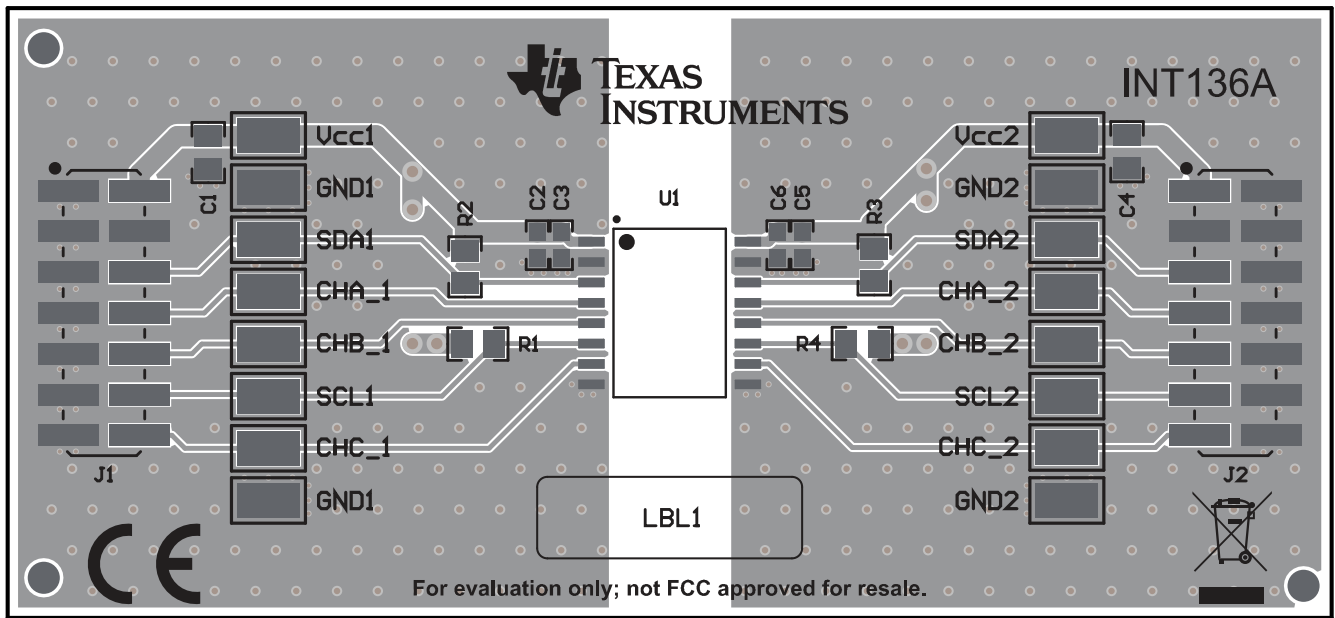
ISO1644DWEVM 顶层 PCB 布局
